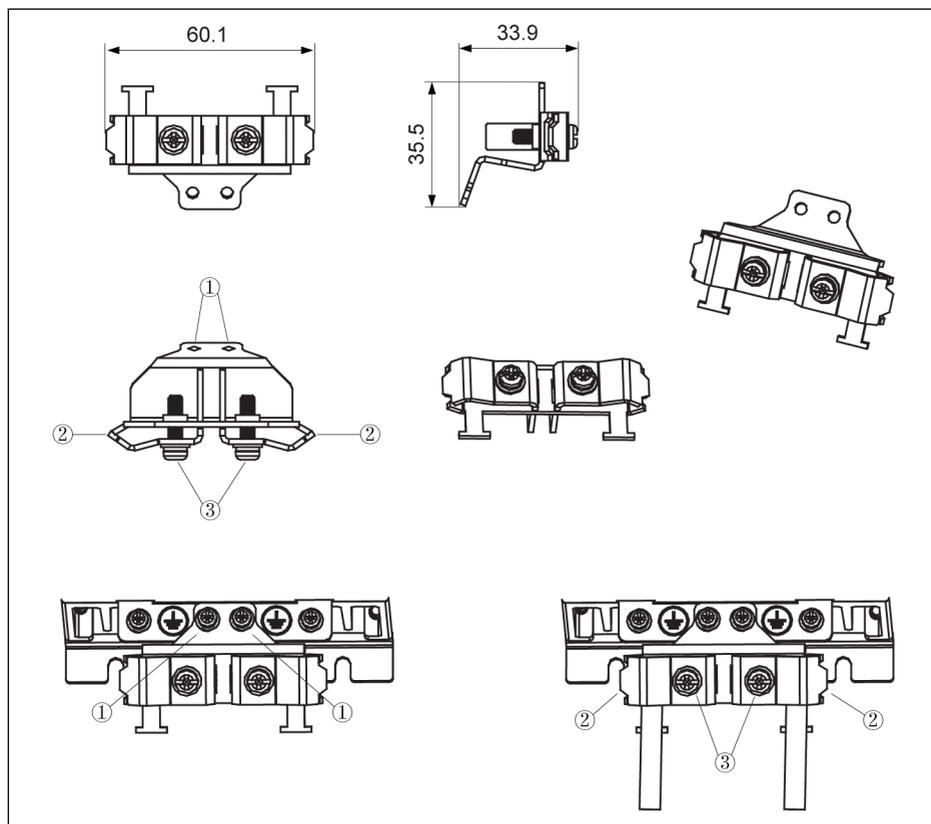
Conexión del cable apantallado con accesorios para 0K40...4K00
